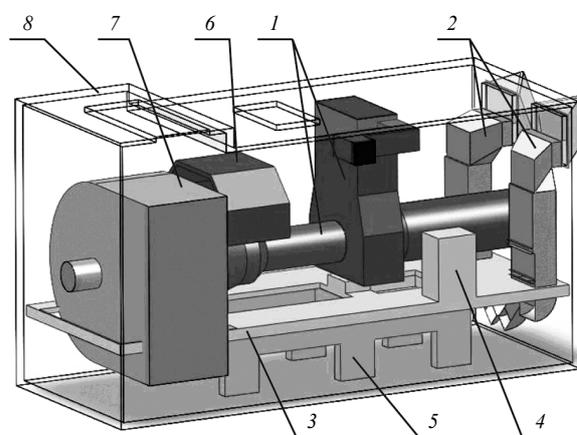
Типовая конструкция ГПА: 1 – газотурбинная установка с улиткой; 2 – воздухопроводы; 3 – пол КШТ; 4 – ящик агрегата зажигания; 5 – фундамент рамы двигателя; 6 – защитный экран; 7 – улитка выхлопного устройства ГПА; 8 – кожух шумотеплоизоляционный
